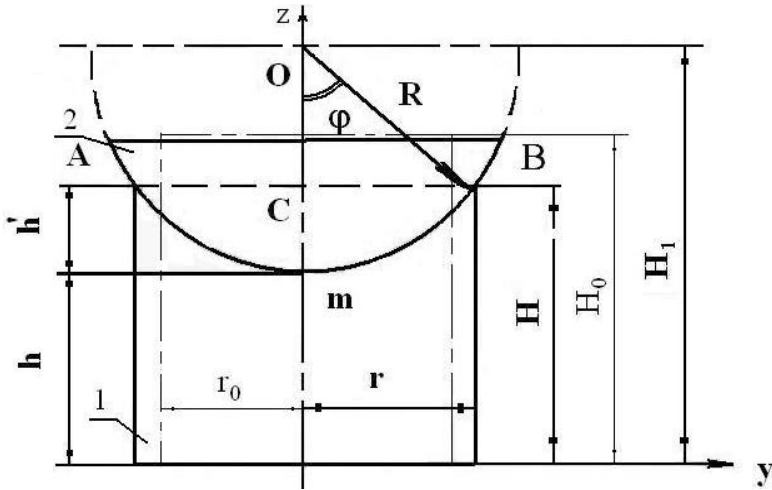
Схема осаджування циліндричної заготовки (1) випуклими плитами (2) [40]
